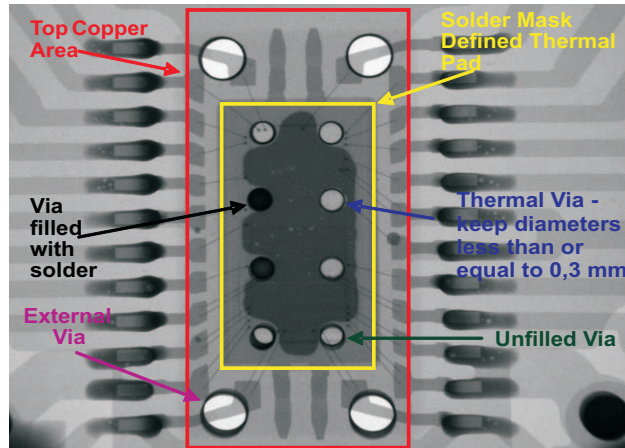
X 射线— 具有内部和外部通孔的 PCB 器件
